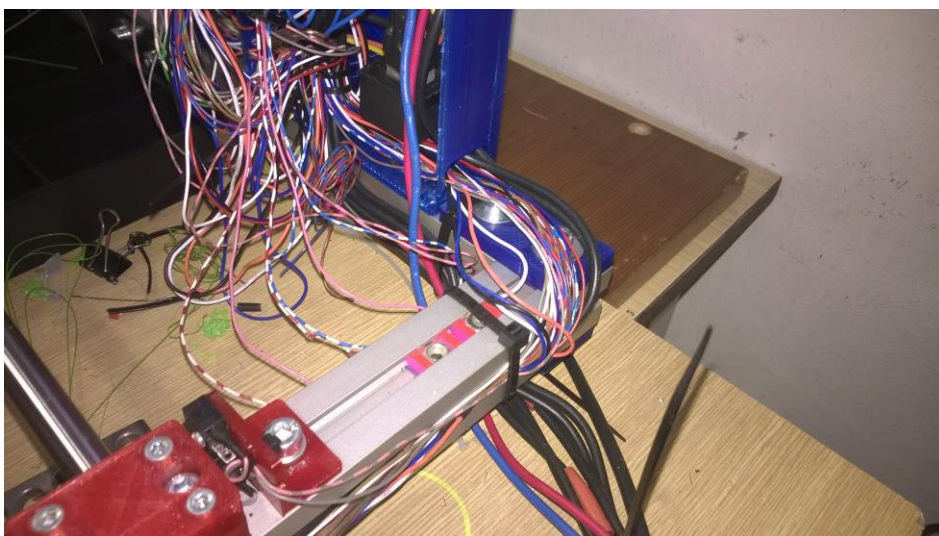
Detail vedení svazku od extruderu 2 a vodičů vyhřívání podložky
